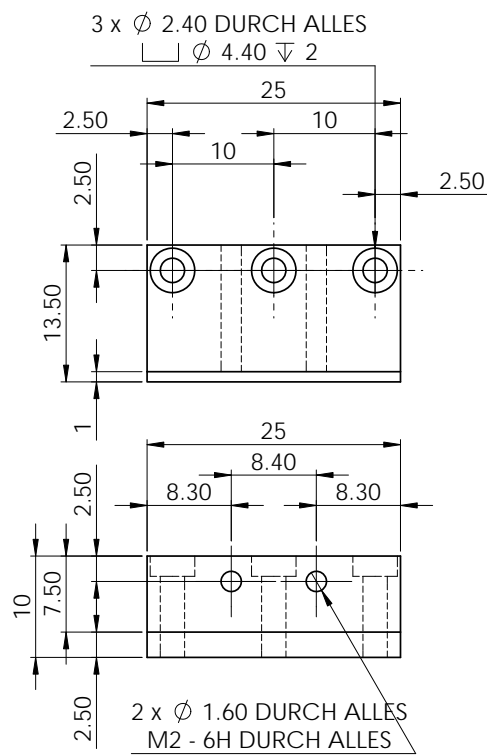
Technische Zeichnung der Probenhalterung.
